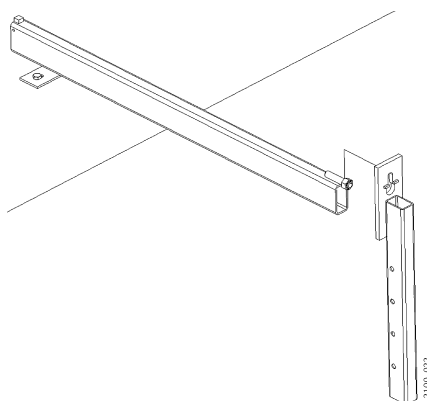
Montage de la fixation à encoches en trou de serrure sur la poutre
